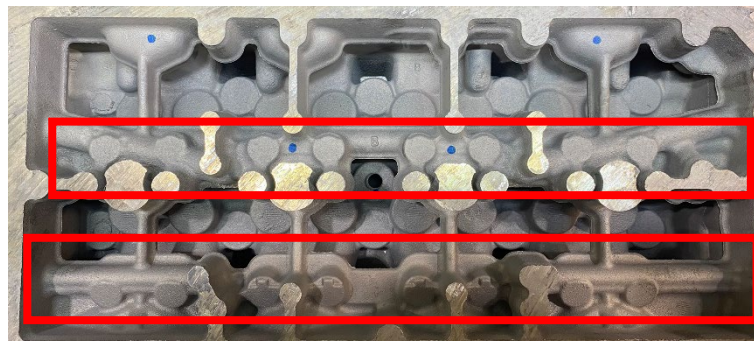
Cabeza de motor vista de galería. Cortesía (NEMAK)
